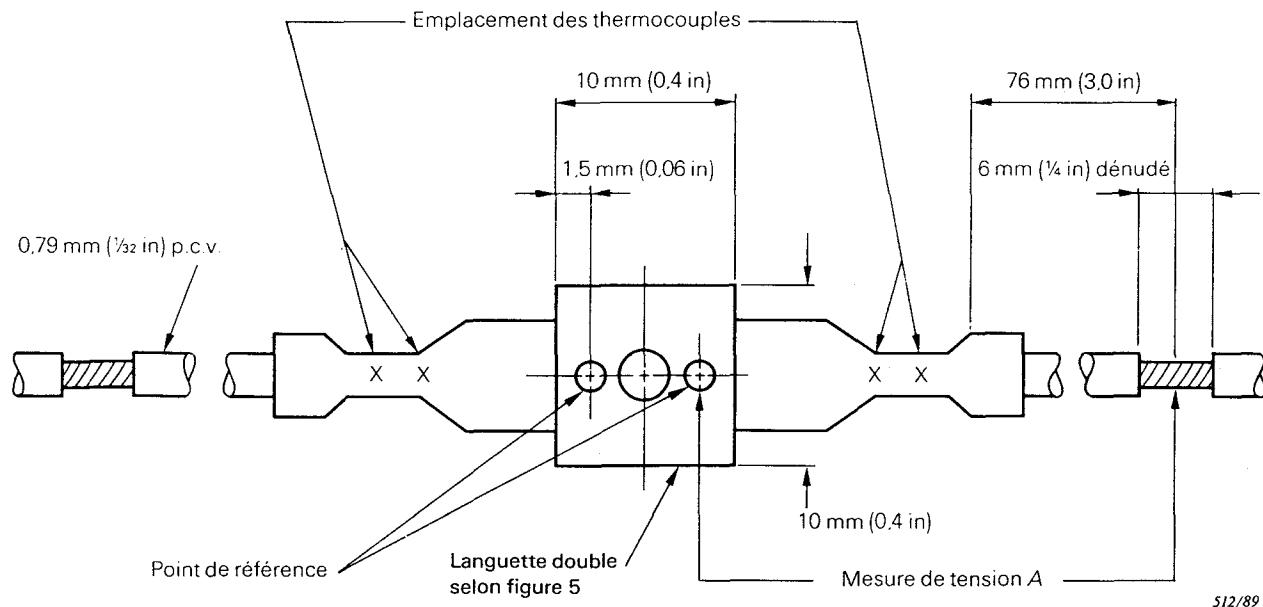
Emplacement des points d'essai et des thermocouples.
